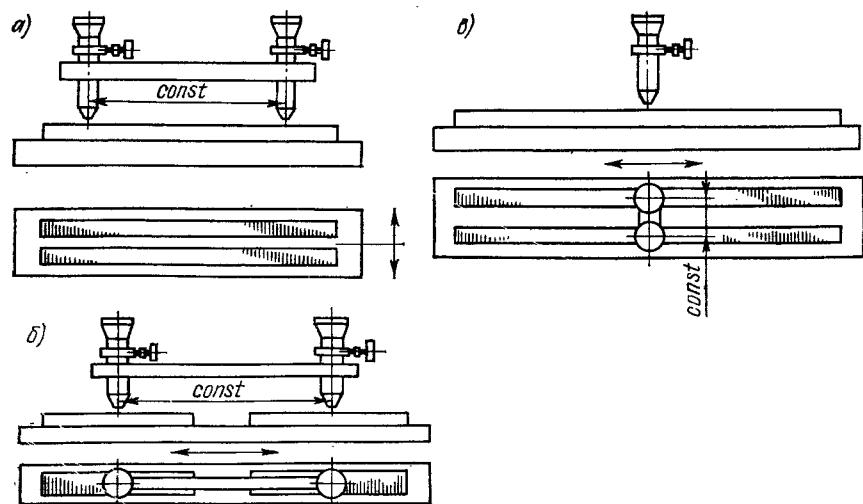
Компараторы: а — поперечный; б — продольный с последовательным расположением шкал; в — продольный с параллельным расположением шкал
